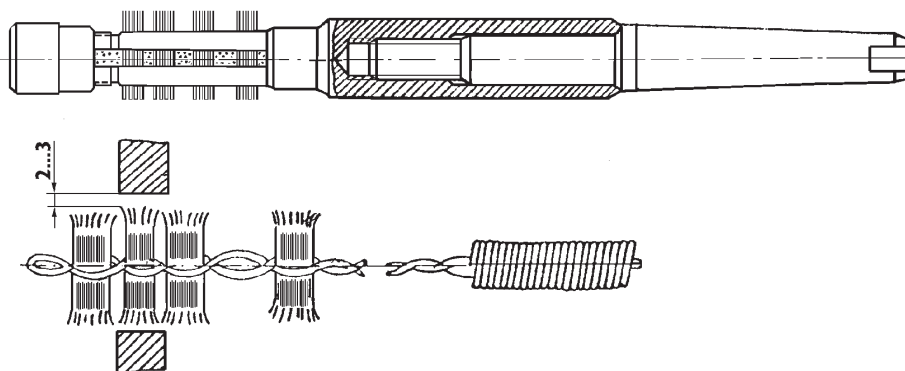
Приспособления для зачистки отверстий в трубных досках
